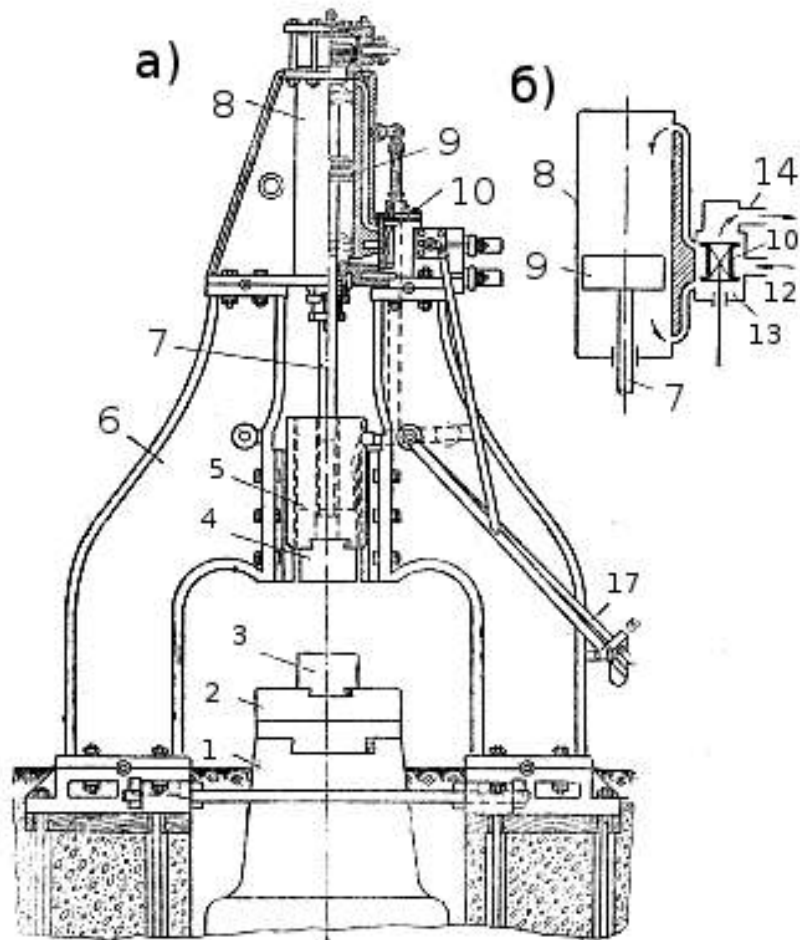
Арочный паровоздушный ковочный молот и распределитель: а — схема молота; б — схема распределителя.
